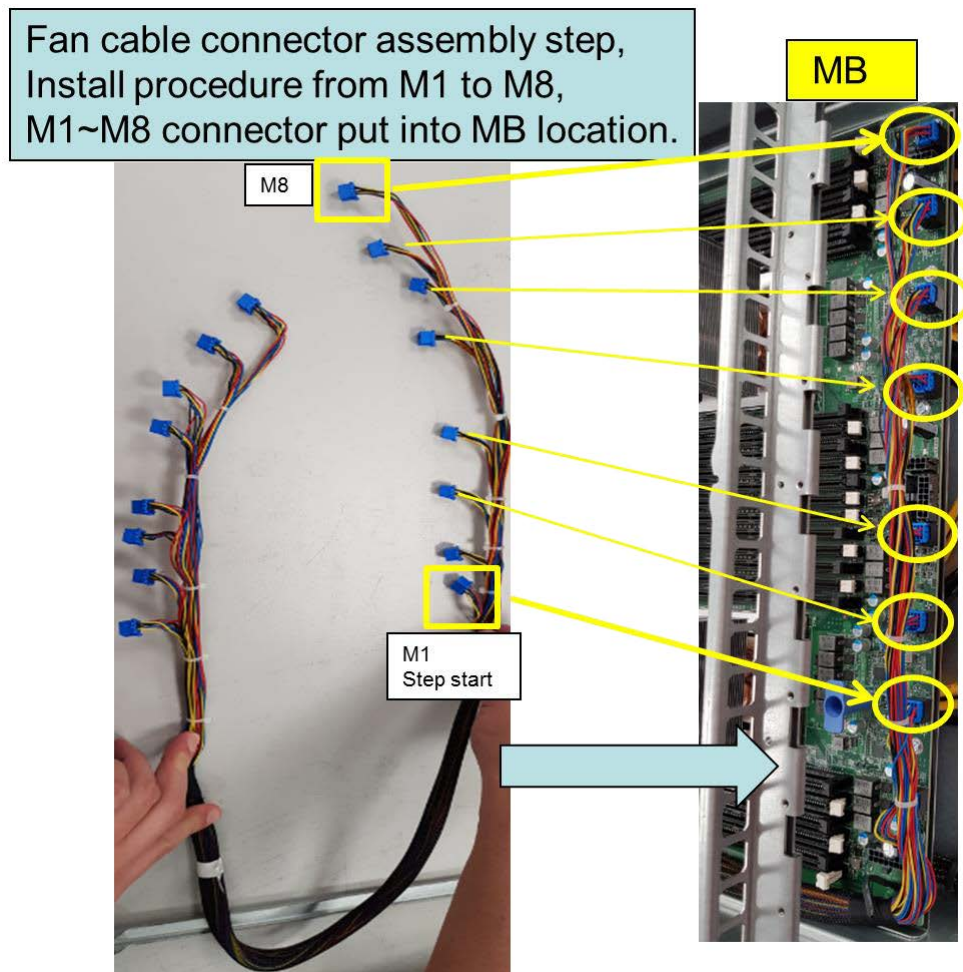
MB del cable del ventilador: ensamblaje de PDB a MB
